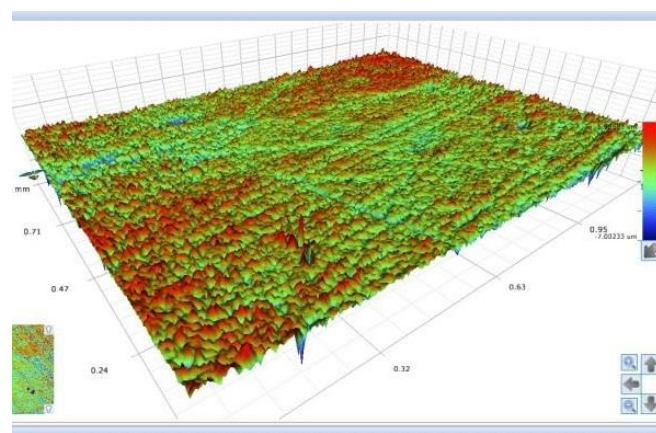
3D-модели поверхностной шероховатости на участках образца
